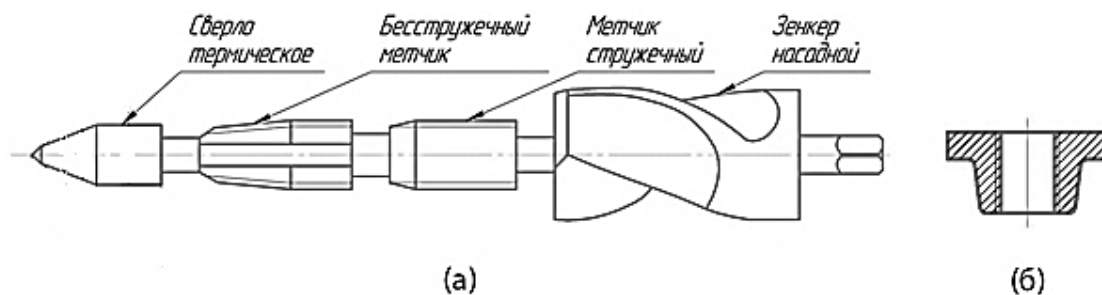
Схема конструкции комбинированного инструмента первого типа
